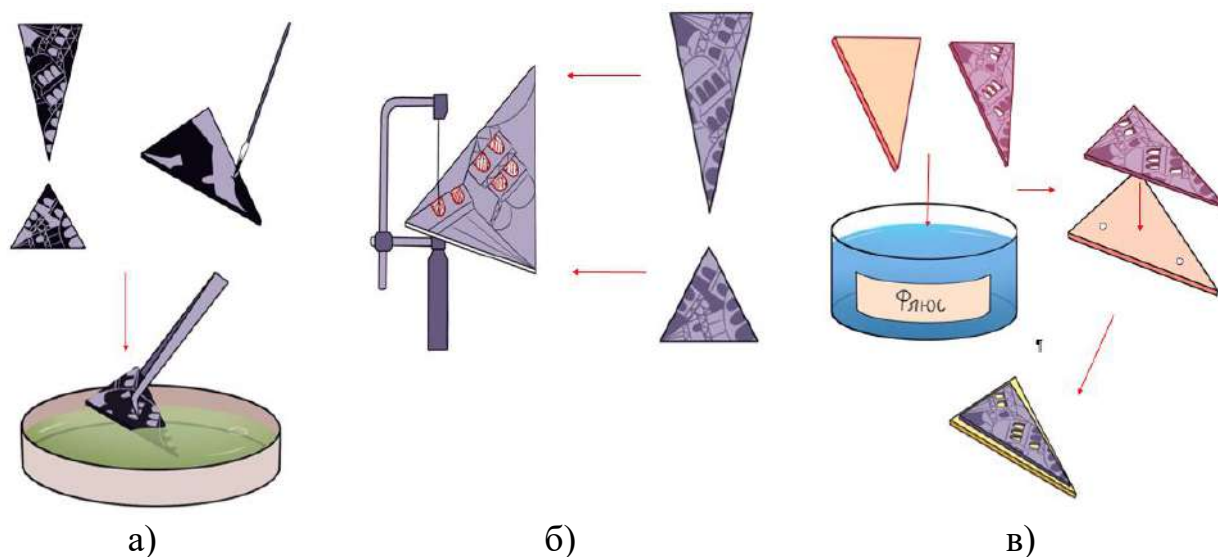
Эскизы процесса для технической карты, iPad 11 pro редактор «iArtbook»: а – процесс травления; б – процесс выпиливания окон; в – процесс пайки деталей
